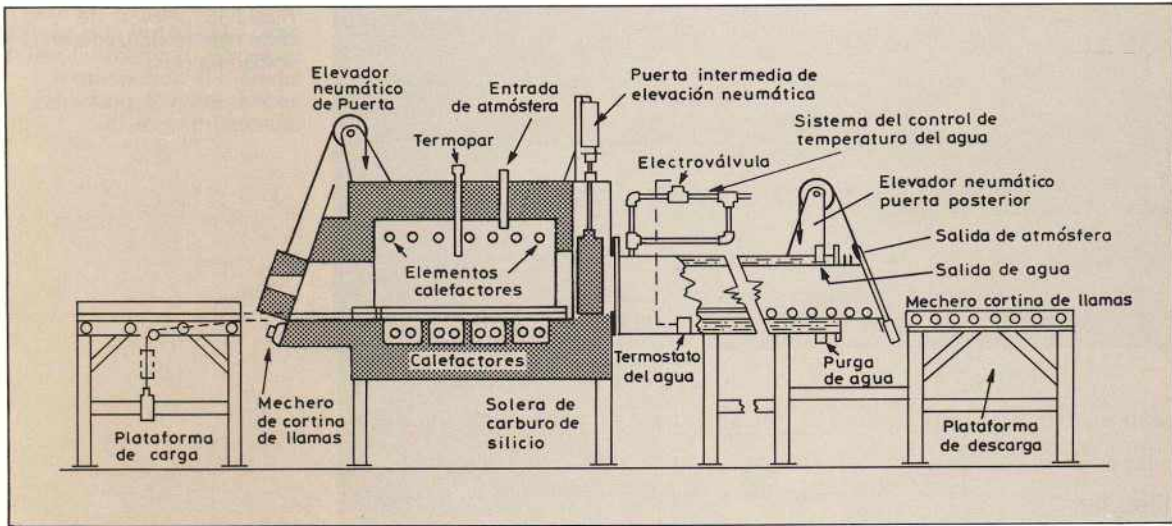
Horno de atmósfera controlada utilizado para la soldadura dura.
